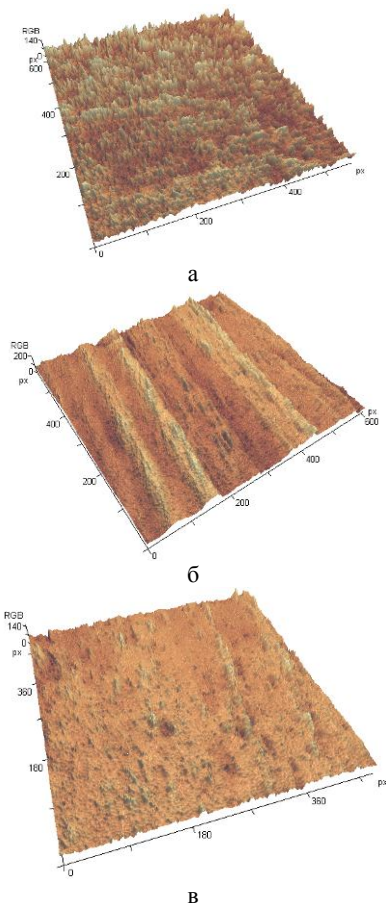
3D поверхность после торцевого фрезерования:
